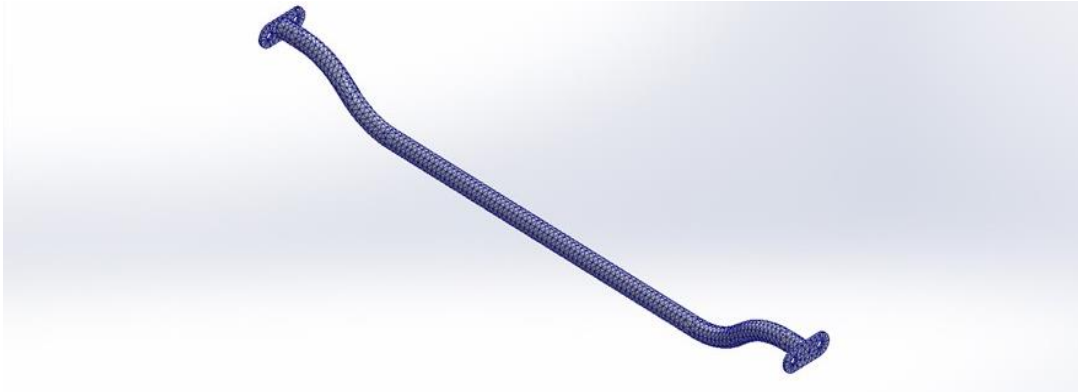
Análisis estático de elemento 5.1 Abrazadera monkey bar. Fuente: Elaboración propia
